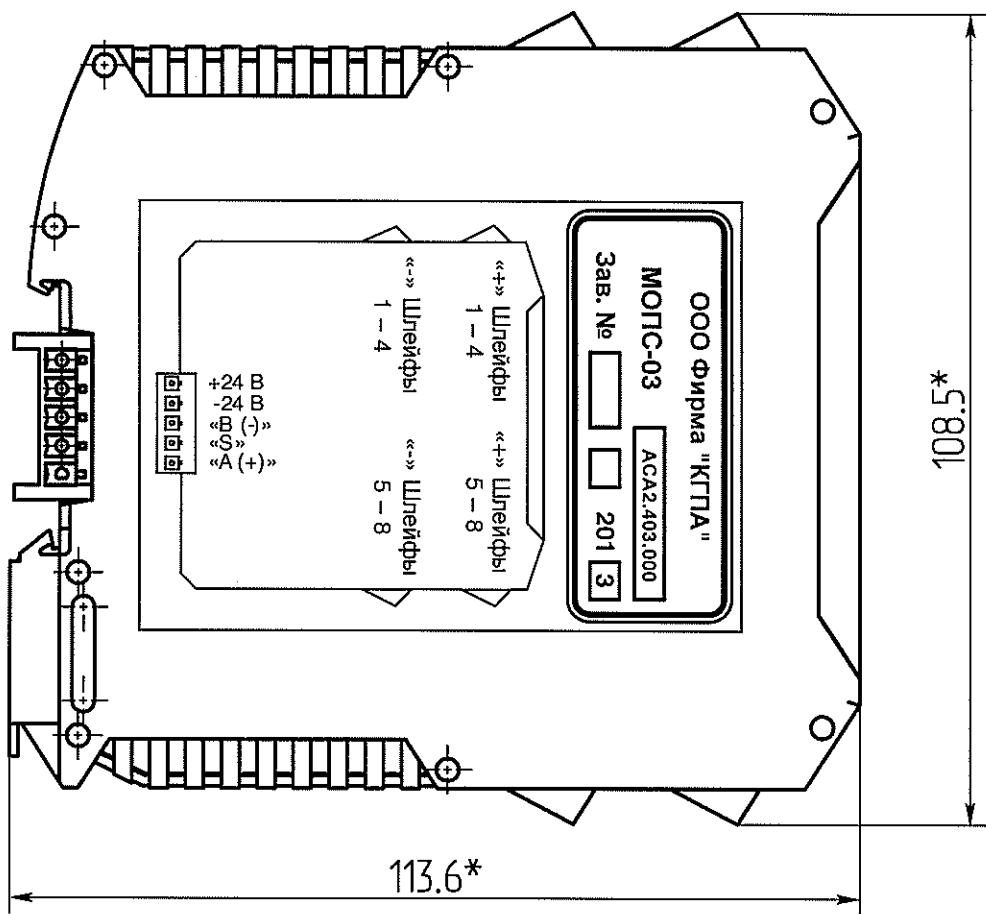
Внешний вид модуля МОПС-03 с шинным соединителем (вид сбоку)
